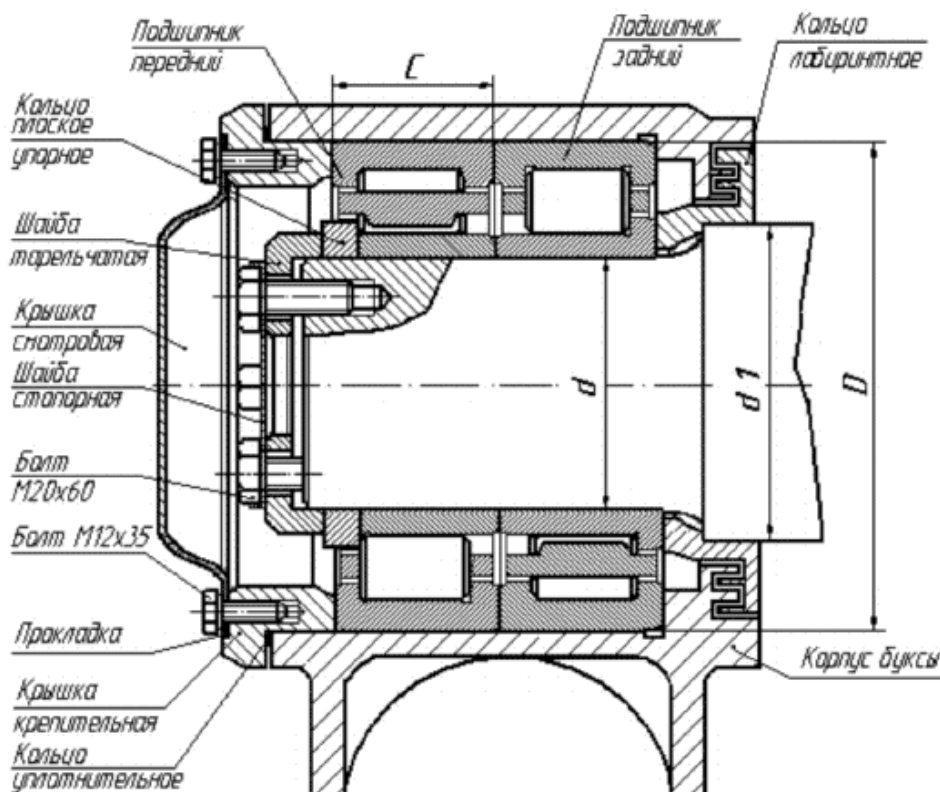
Схема буксового узла с подшипниками роликовыми цилиндрическими с торцевым креплением шайбой тарельчатой и болтами M20
